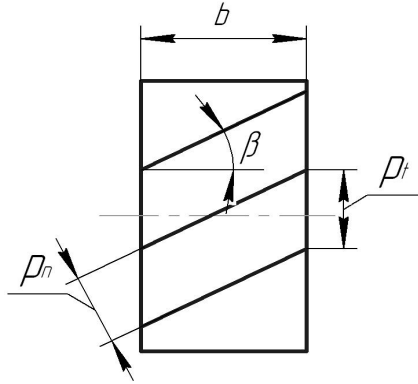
Коловий і нормальний кроки косозубого колеса
